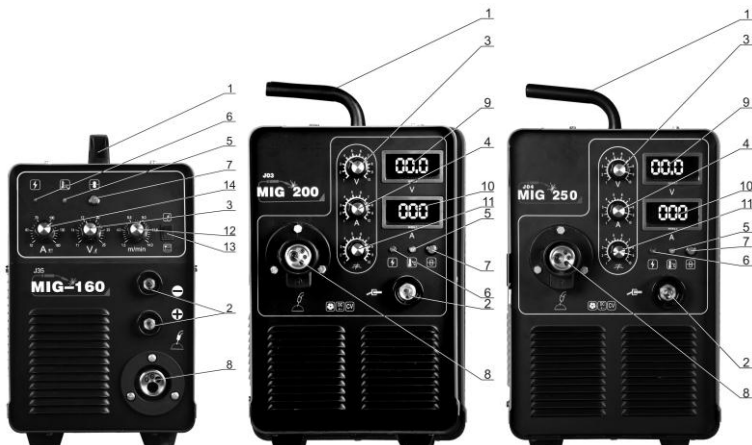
Лицевая панель полуавтоматов сварочных MIG-160/MIG-200/MIG-250
